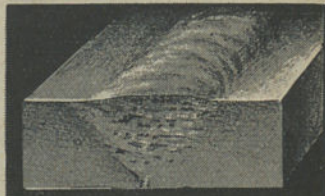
Colagem na base e placas de oxido, na soldadura.
